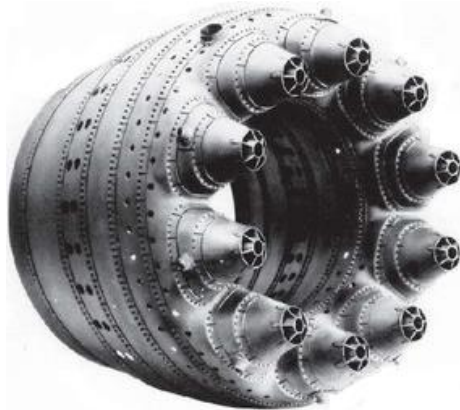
Корпус кольцевой камеры сгорания двигателя АИ-20
